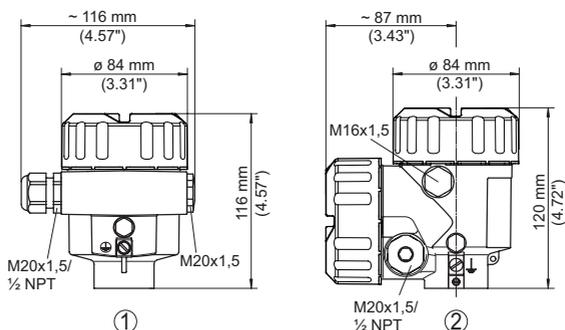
Корпуса в исполнении IP66/IP68 (0,2 bar), (с установленным модулем индикации и настройки корпус выше на 9 mm/0.35 in)
